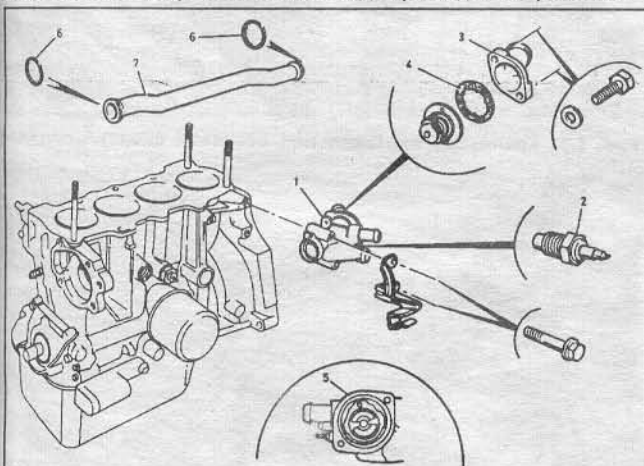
Термостат и соединительные детали: 1 - корпус; 2 - температурный датчик; 3 - крышка корпуса; 4 - прокладка; 5 - термостат; 6 - резиновое кольцо; 7 - входная труба водяной помпы.
